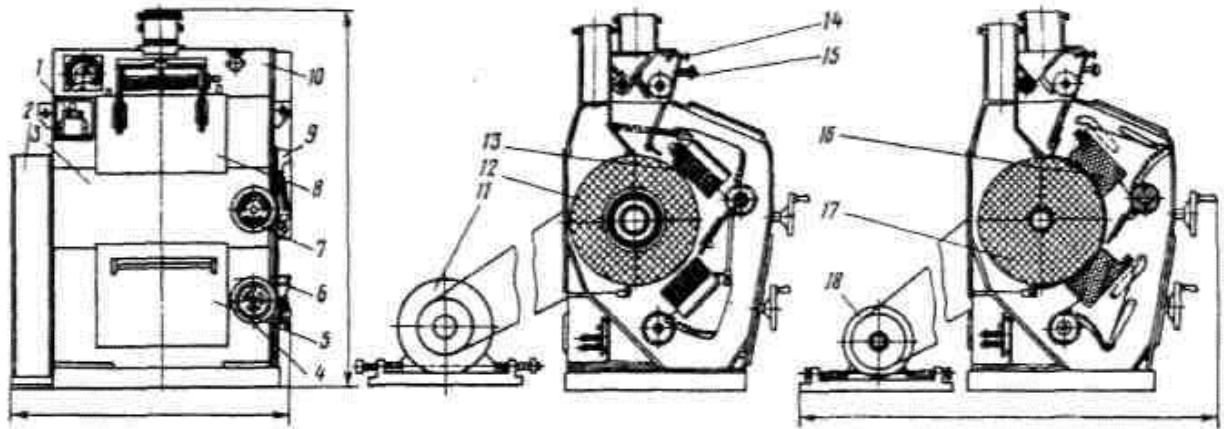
Шелушильный станок 2ДШС-3: 1 — пульт управления; 2 — ограждение; 3 — станина; 4, 7 — штурвалы; 5, 8 — дверки; 6, 9 — рычаги управления; 10 — питающий механизм; 11, 18 — электродвигатели; 12 — абразивный валок (валец); 13 — резиновая дека; 14 — задвижка; 15 — ручка маховика для регулирования производительности; 16 — песчаниковая дека; 17 — песчаниковый валок (валец).
